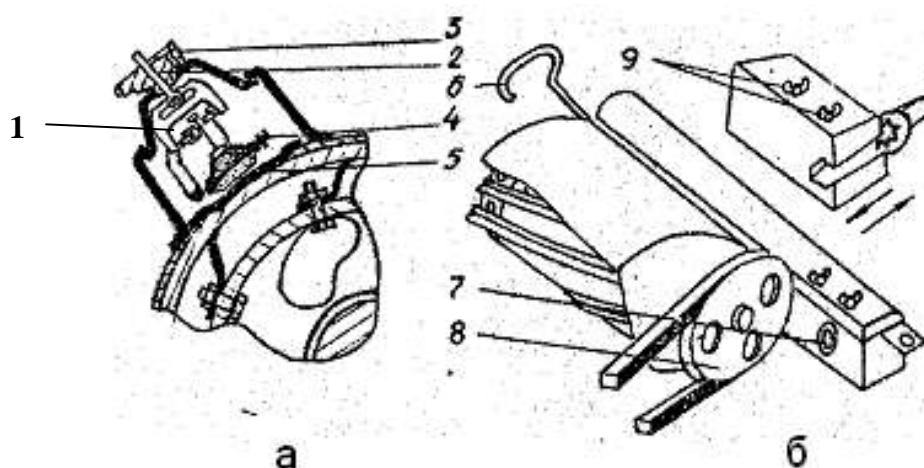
Заточное устройство: а – заточка ножей режущего барабана; б – аппарата вторичного резания: 1 – каретка; 2 – штурвал; 3 – собачка; 4 – сегмент; 5 – заслонка; 6 – тяга; 7 – фрикционное кольцо; 8 – шкив; 9 – гайки-барашки
